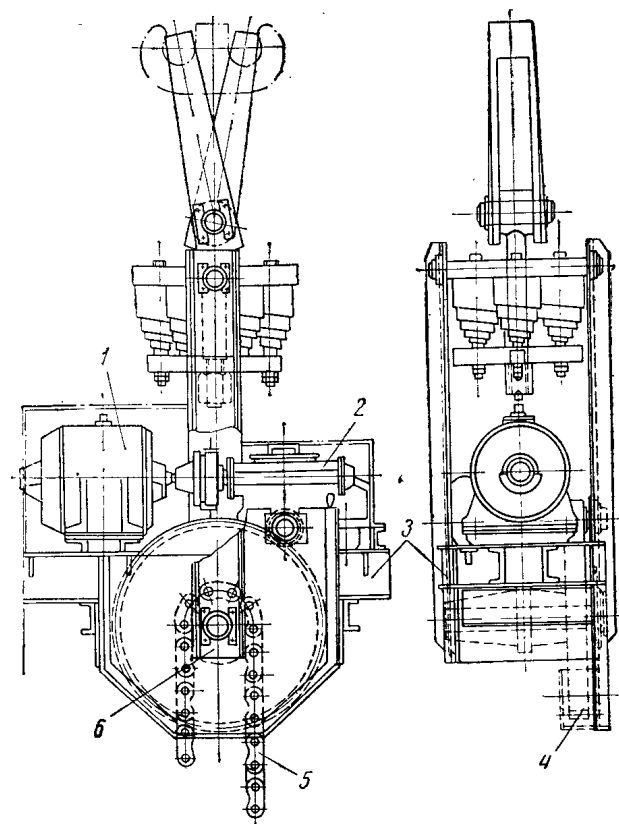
Электрический подвесной кантователь: 1 — электромотор, 2 — редуктор, 3 — рама, 4 — зубчатое колесо, 5 — цепь, 6 — узел звездочки
